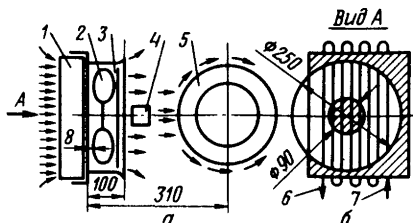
Схема холодильного агрегата ВСр400 1 (вид сверху):
